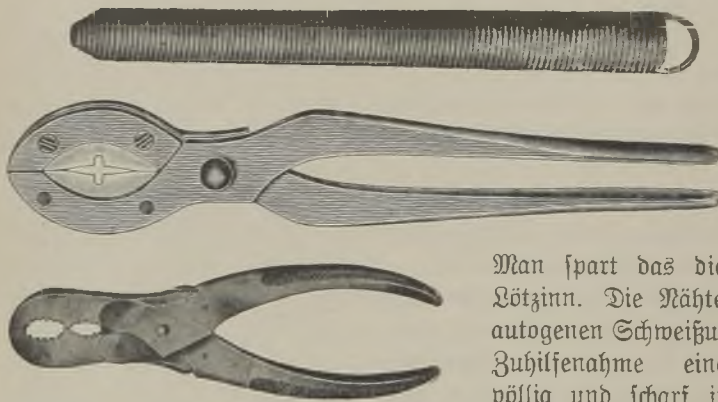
Werkzeuge für Bleirohrbearbeitung. Biegespirale und Rohrzanzen. (Hahn & Kolb, Stuttgart.)
